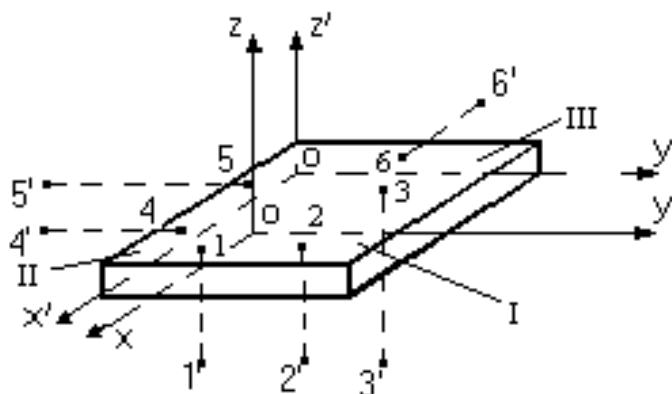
Комплект баз I, II, III і опорні точки 1,2,3,4,5,6 з двосторонніми зв'язками призматической заготовки: 1', 2', 3', 4', 5', 6' - проекції опорних точок на координатні площини
